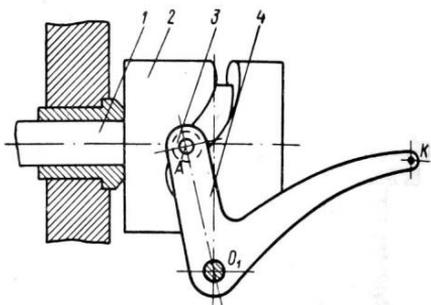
Рычажно-кулачковый механизм нитепритягивателя
